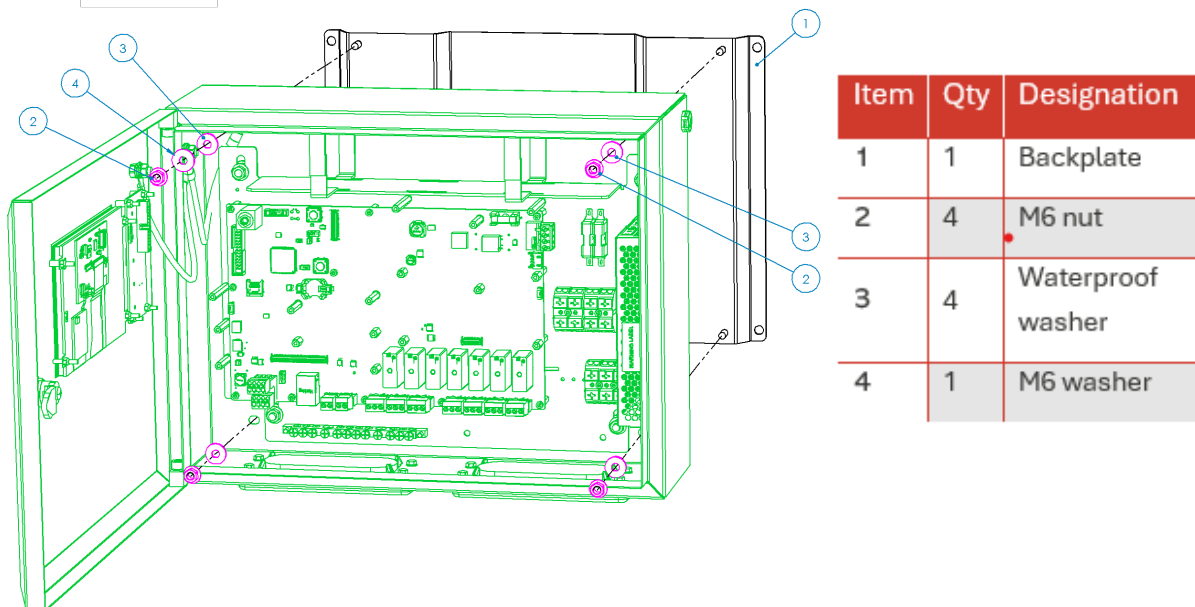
Montage de l'unité de commande sur la plaque arrière
